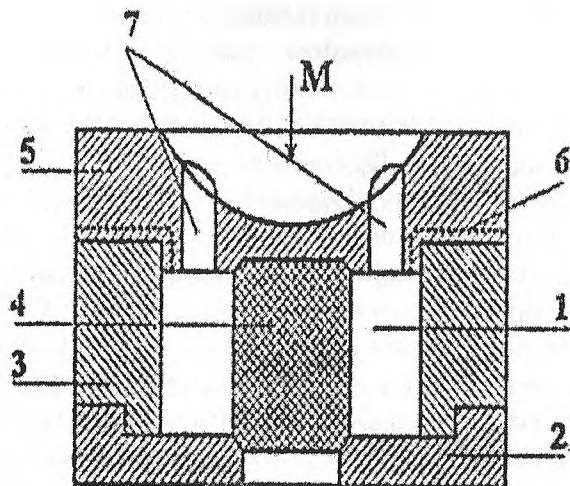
Эскиз разреза металлической формы – кокиля
